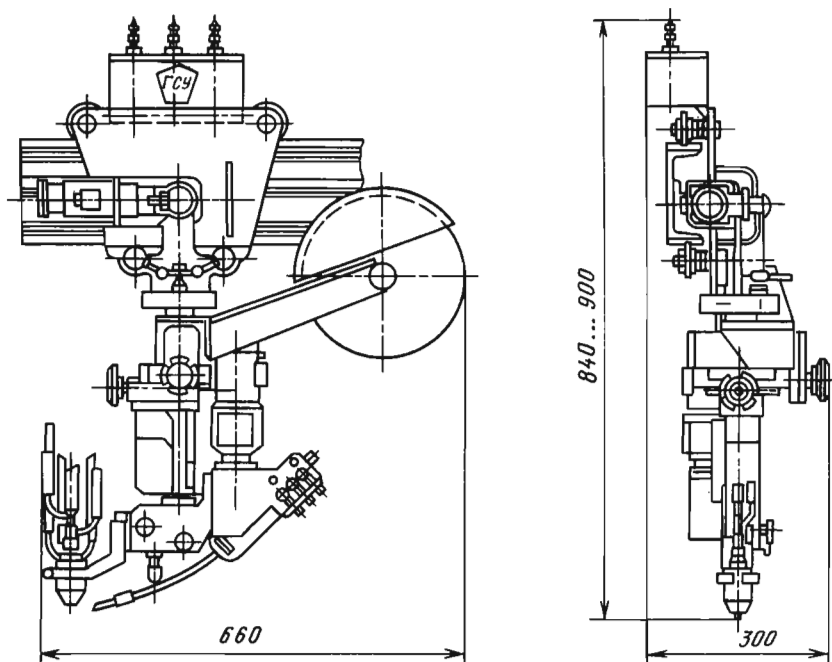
Самоходная подвесная головка ГСУ-7 для сварки продольных швов изделий из алюминиевых сплавов сжатой дугой с подачей присадочной проволоки
